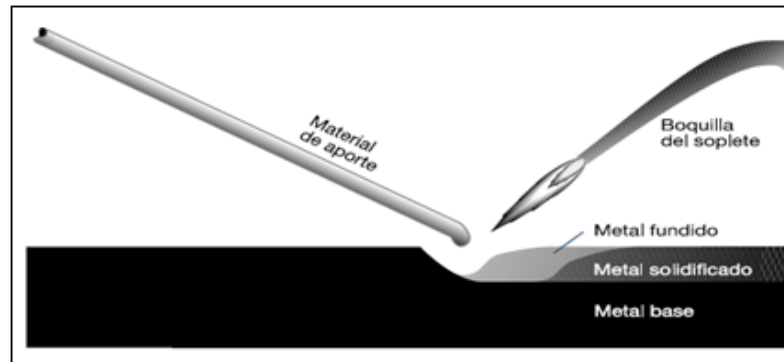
Proceso de soldadura oxiacetilénico
